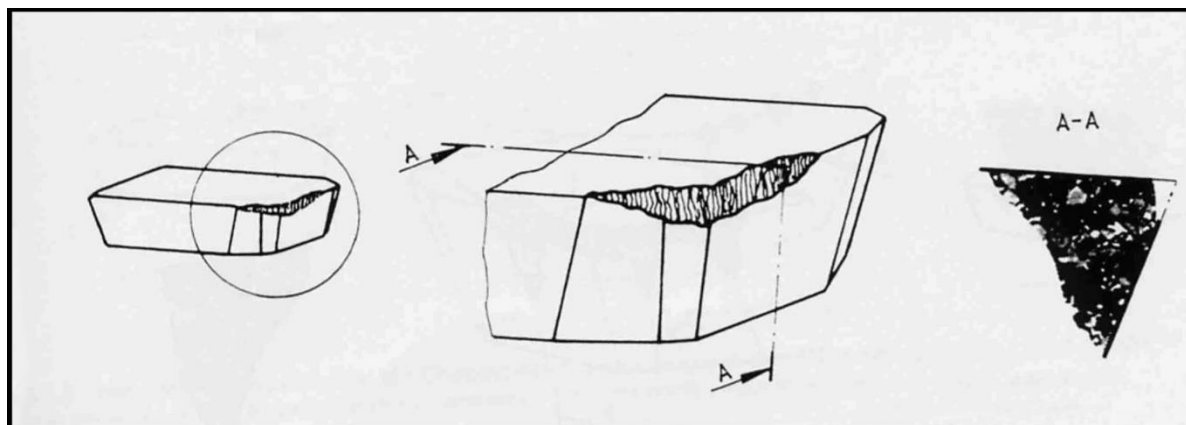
Representação do desgaste de flanco uniforme e sua vista de corte (ISO-8688-1, 1989)
